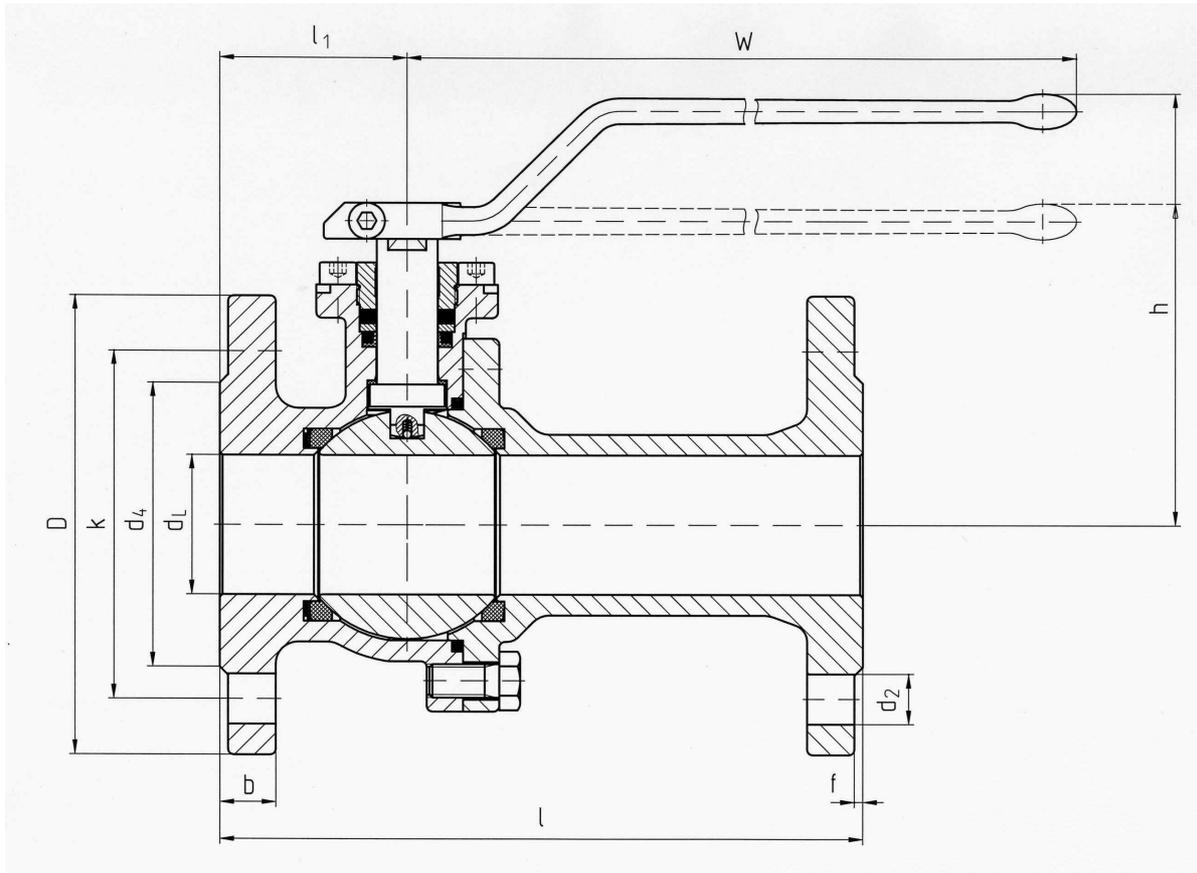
Kugelhahn mit Flanschanschluss nach DIN EN 1092-1 Form B1; Baulänge Grundreihe 28 (lang) nach EN 558-1 (F17 nach DIN 3202 Teil 1)
